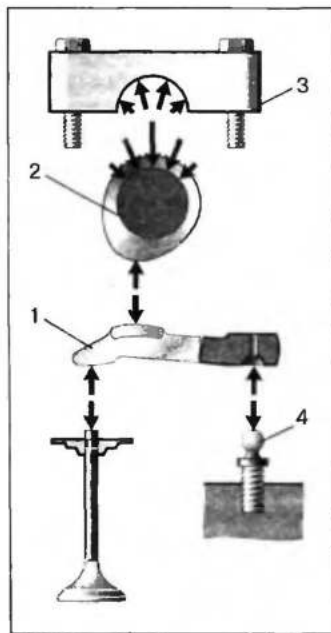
Усилия на детали в схеме привода клапана рычагом: 1 — рычаг; 2 — распределительный вал; 3 — опора распределительного вала (крышка); 4 — опора рычага
